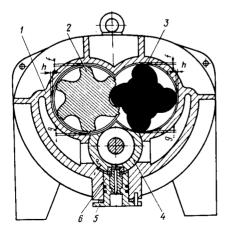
Винтовой компрессор (сборка): 1 — корпус; 2 — ротор ведомый; 3 — ротор ведущий; 4 — золотник регулятора производительности; 5 — кольцо регулировочное; 6 — стакан
